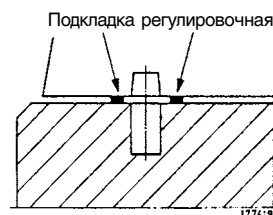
Размещение регулировочных прокладок под опорной плитой
